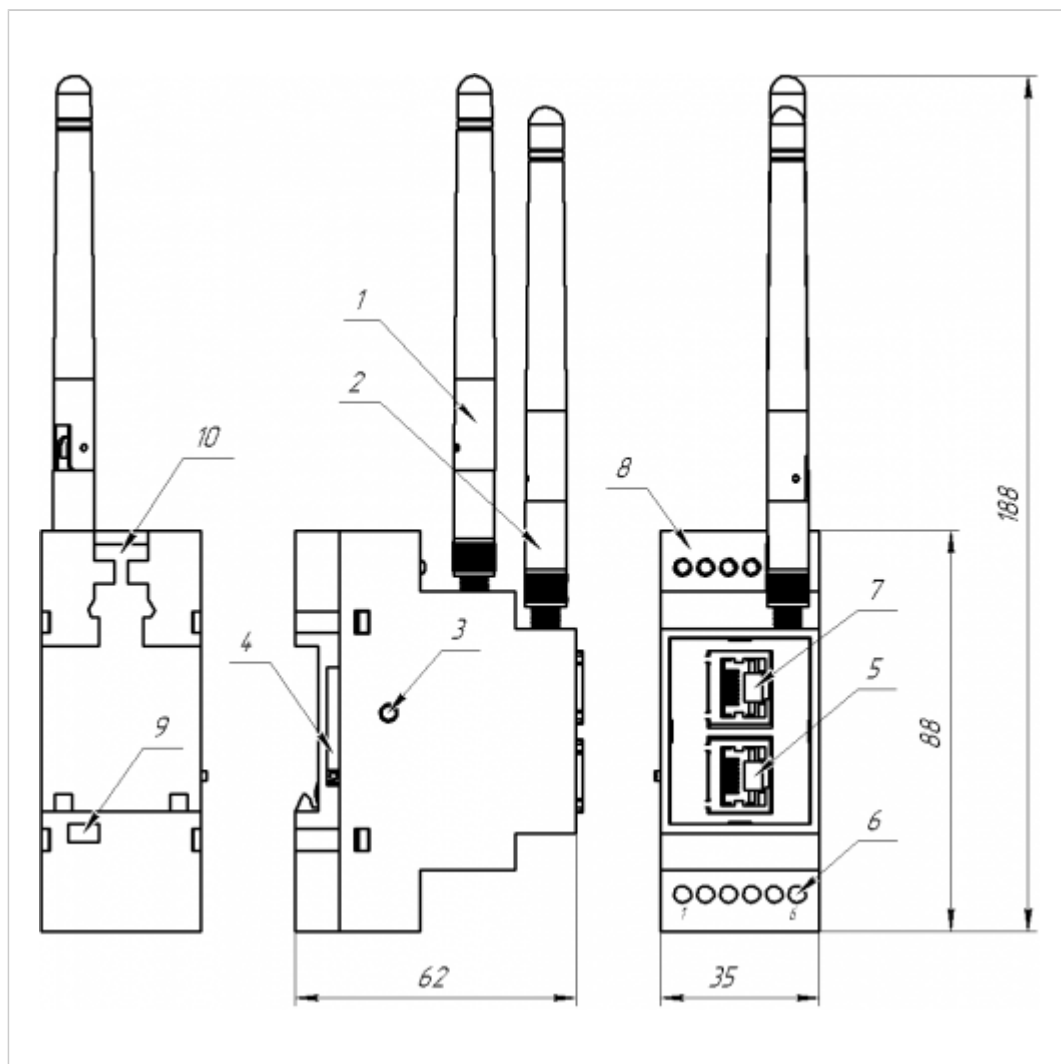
Габаритные размеры и позиционные обозначения СК-01
